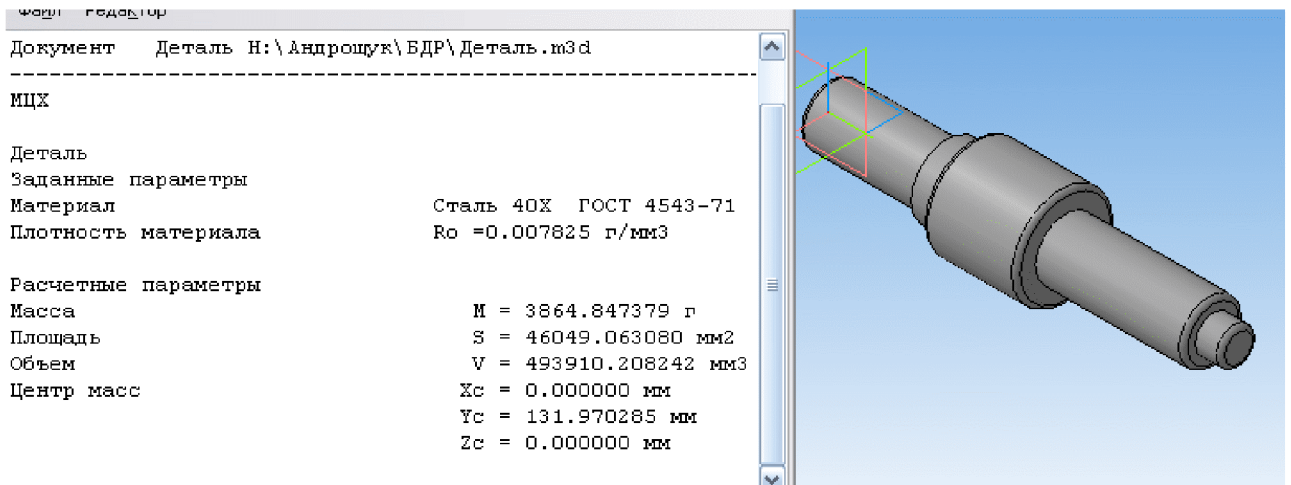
Визначення маси заготовки штампованої на КГШП
